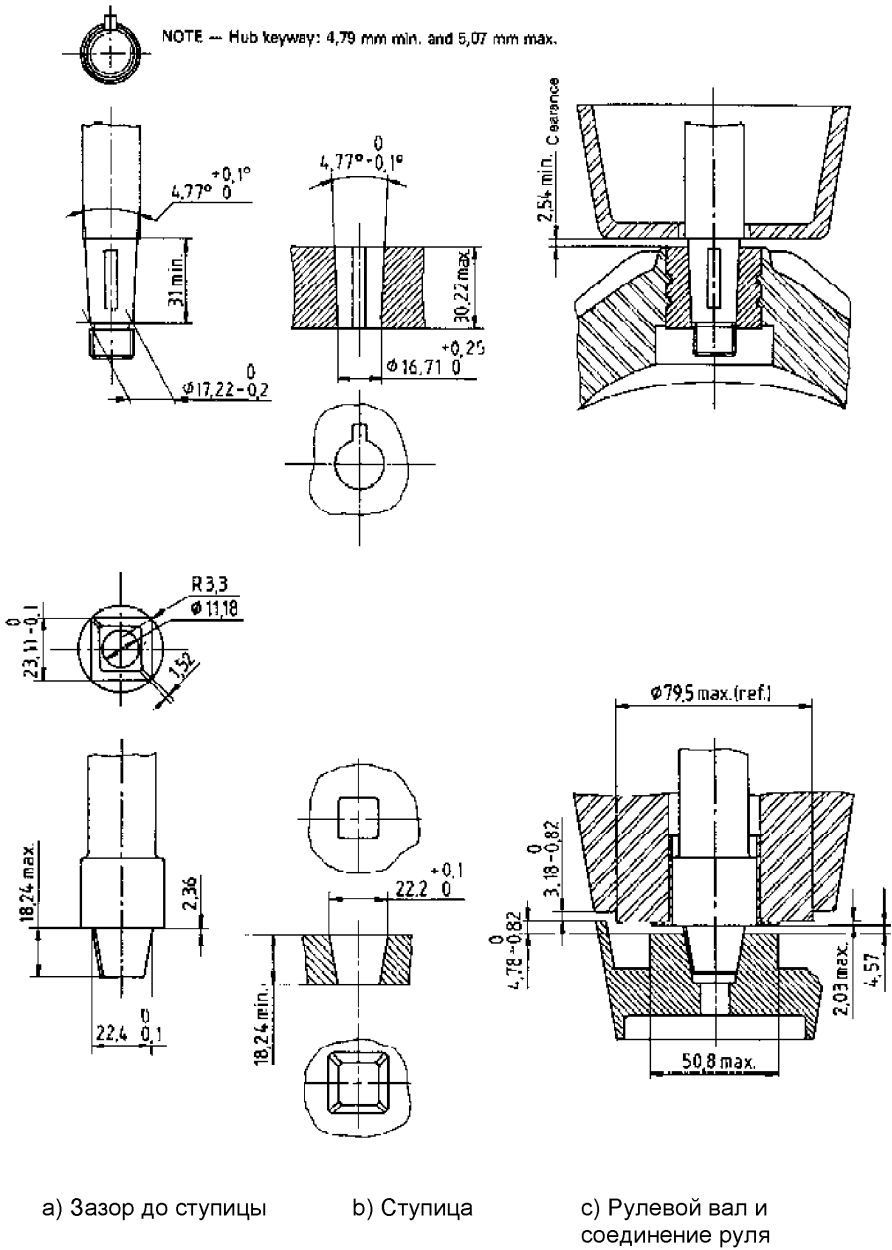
Рулевой вал и ступицы рулевых колес
